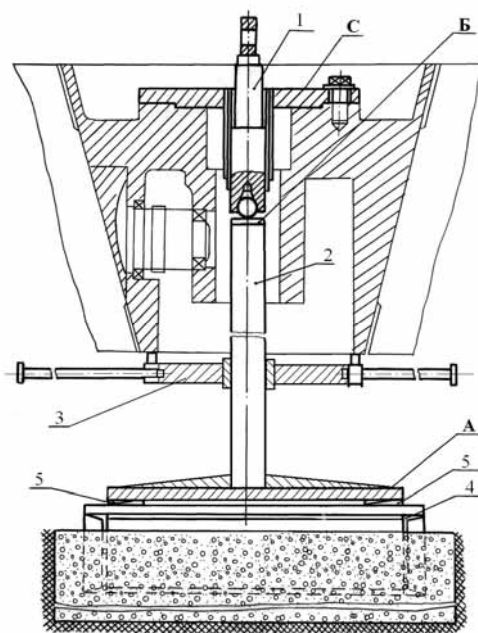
Стенд статической балансировки рабочих колёс лопастных насосов
